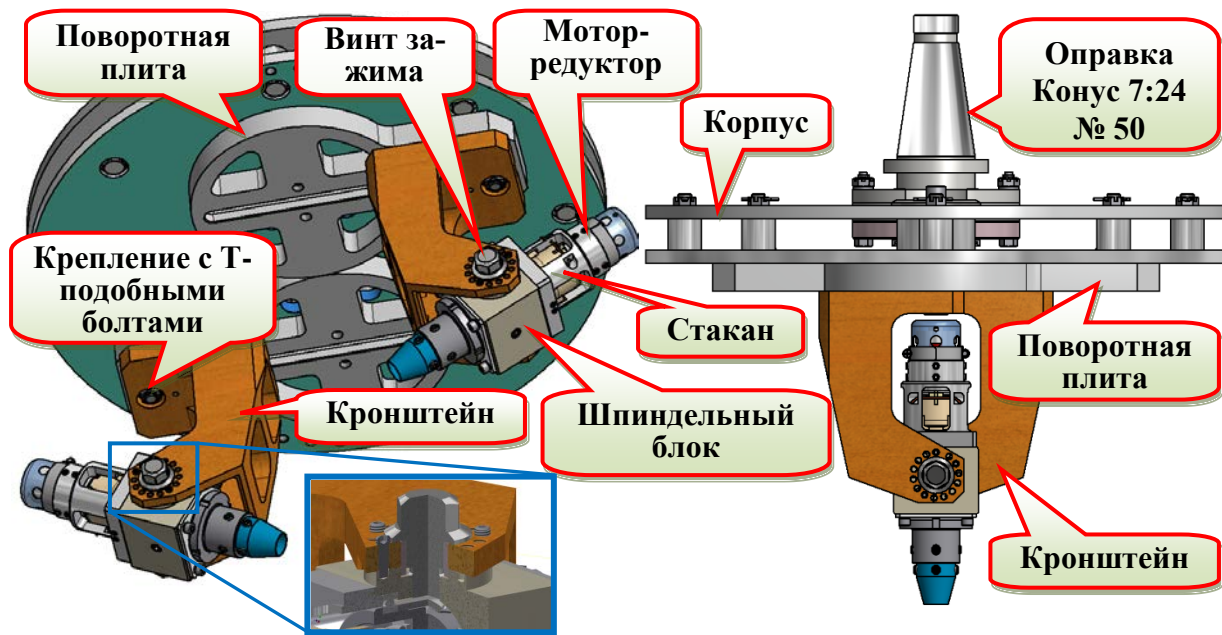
Общий вид роторной головки для магнитно-абразивной обработки
